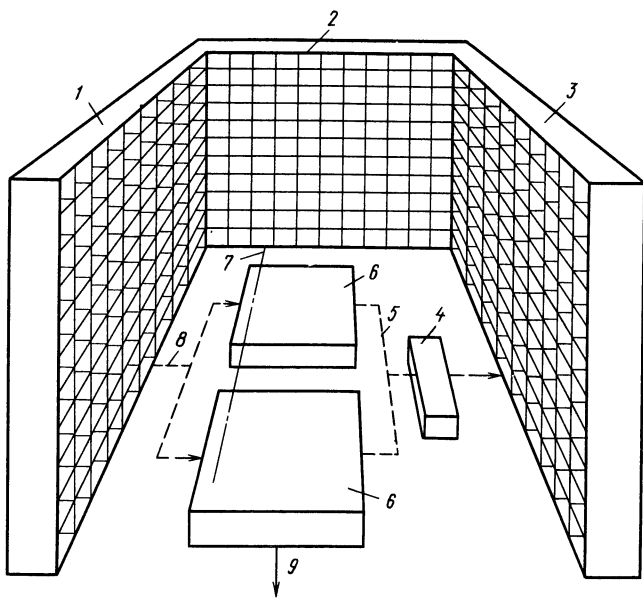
Компоновка АТСС с тремя стеллажами:
